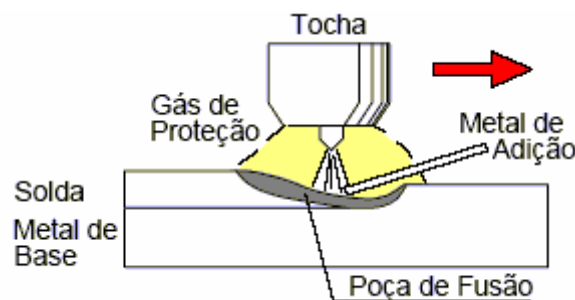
Soldagem TIG (MODENESI e MARQUES, 2000)
